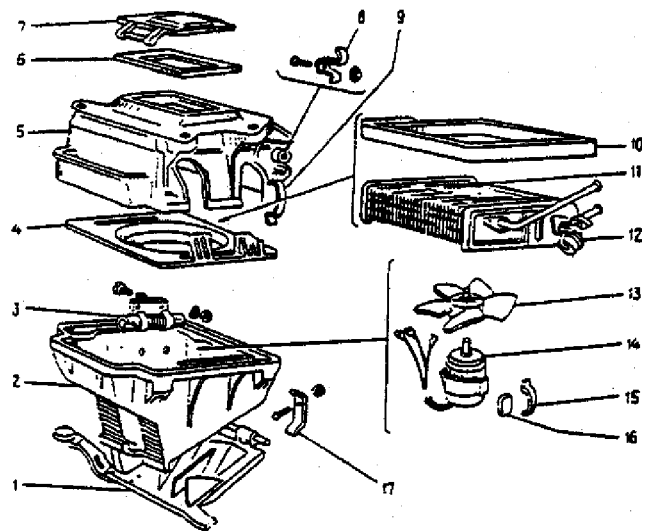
Componentes da caixa da ventilação: 1 - tampa de distribuição do ar; 2 - carcaça do ventilador; 3 - resistor complementar; 4 - tampa do ventilador; 5 - caixa do radiador; 6 - junta; 7 - tampa do fluxo de ar; 8 - presilha de fixação dos tubos de alimentação; 9 - presilhas elásticas; 10 - guarnição de vedação do radiador; 11 - radiador; 12 - válvula; 13 - ventoinha; 14 - motor elétrico; 15 - presilhas elásticas; 16 - coxim do motor elétrico; 17 - presilha de fixação da tampa de distribuição de ar.
